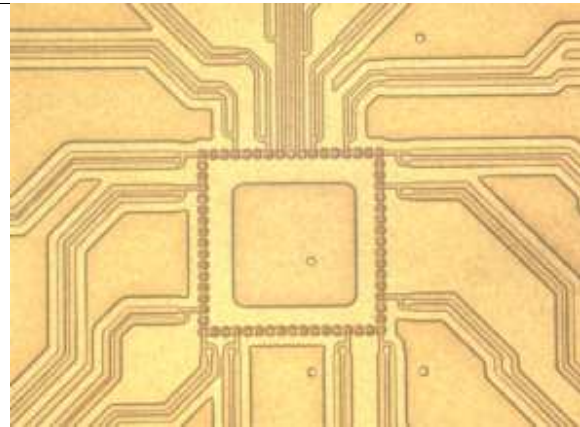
Plage d'accueil puce de 2 mm avec 100 µm de pas (panoplie 35 mm).
